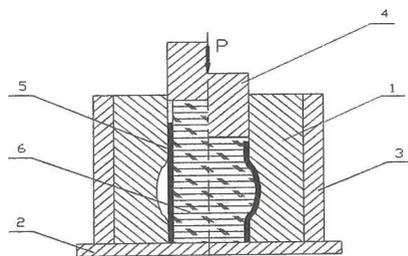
Штамп для раздачи трубчатой заготовки с использованием стержня из льда или снега
